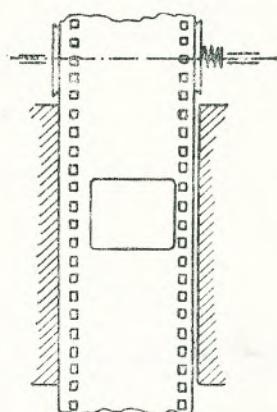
Схема фильмового канала с роликом и боковой направляющей (кинопроектор КШС-1)
